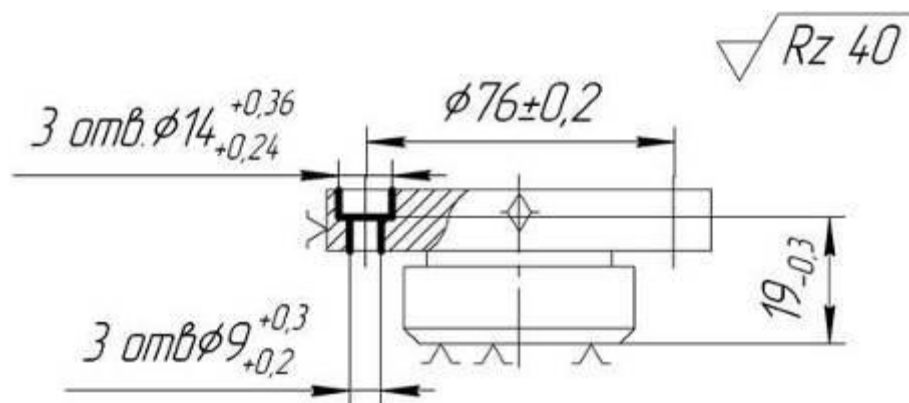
Операция сверления на вертикально-сверлильном станке
